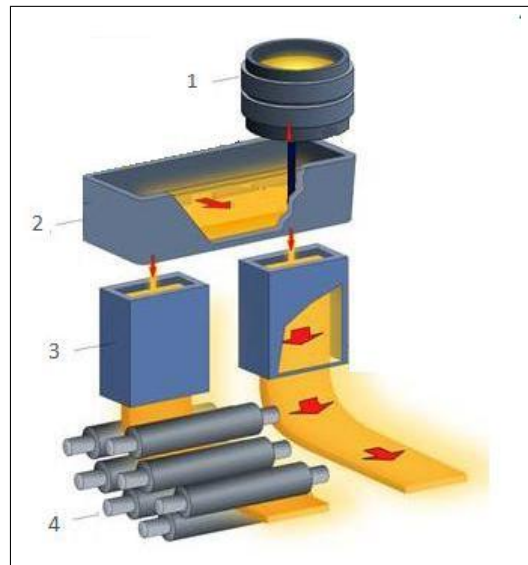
Fonte: Böhrer Welding, adaptado.
